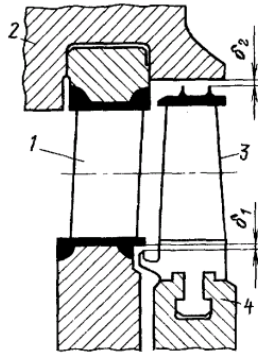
Схема уцілення ступені: 1 – соплова решітка; 2 – корпус турбіни; 3 – робоча лопатка; 4 - диск
